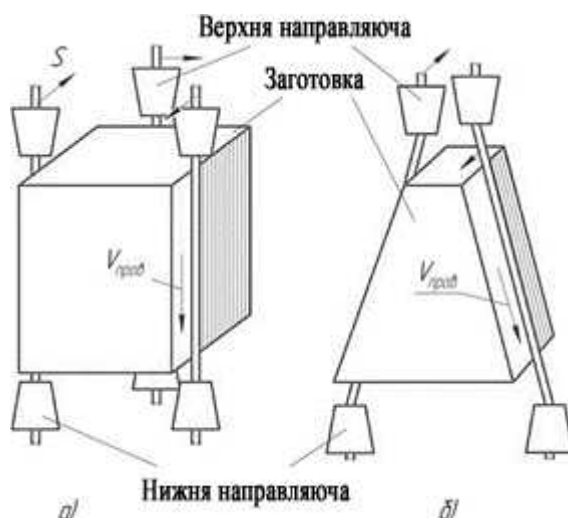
Схема проволочно–різьбового ЕЕ обробки (S – напрямок подачі): а – прямий рез (циліндричний); б – кутовий рез (різка на конус)
